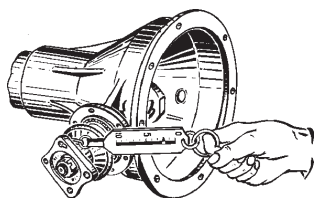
Проверка затяжки подшипников ведущей шестерни
